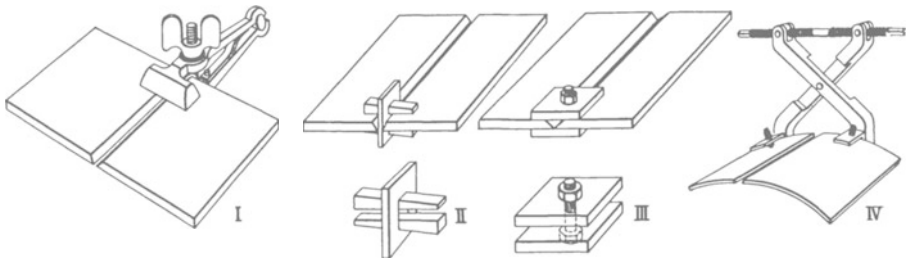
Hilfsvorrichtungen für das Festhalten der Blechränder beim Schweißen.
